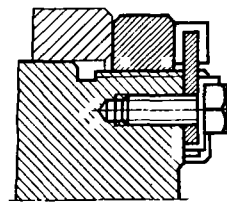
Стопорение кольцевой гайки с торцовым зубом привертной пластиной
